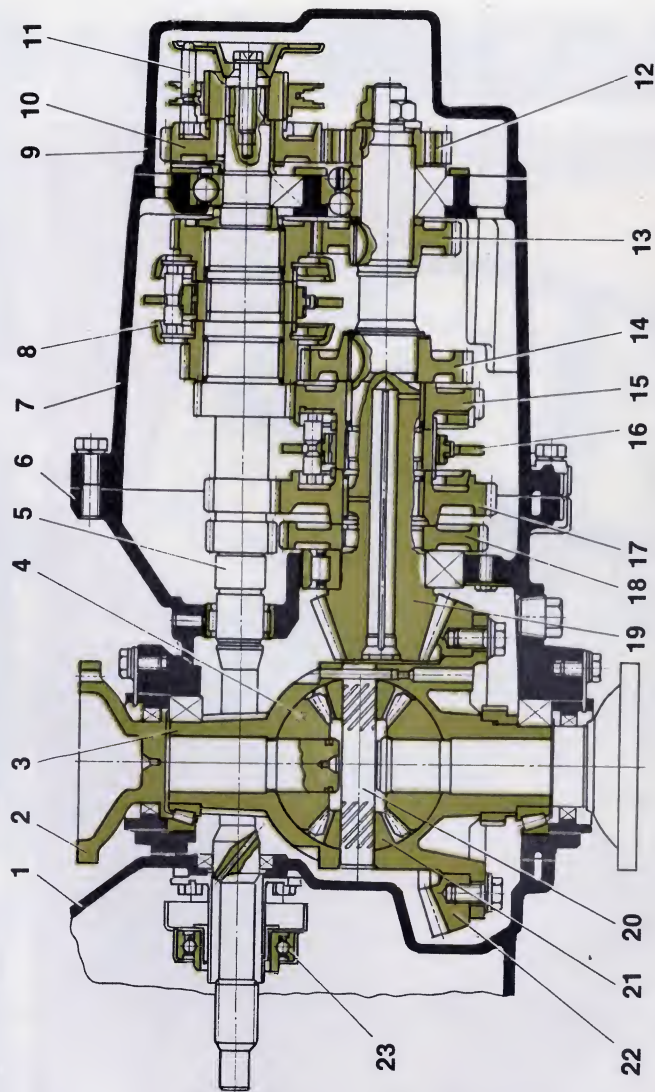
Трансмиссия «Москвича-2141»: 1 — картер сцепления; 2 — фланец полуоси; 3 — коробка дифференциала; 4 — шестерня полуоси; 5 — первичный вал; 6 — картер главной передачи; 7 — картер коробки передач; 8 — синхронизатор III и IV передач; 9 — крышка коробки передач; 10, 12 — шестерни V передач; 11 — синхронизатор V передач; 13 — ведомая шестерня IV передач; 14 — ведомая шестерня III передач; 15 — ведомая шестерня II передач; 16 — синхронизатор I и II передач; 17 — ведомая шестерня I передач; 18 — ведомая шестерня передачи заднего хода; 19 — вторичный вал с ведущей шестерней главной передачи; 20 — ось сателлитов; 21 — сателлит дифференциала; 22 — ведомая шестерня главной передачи; 23 — выжимной подшипник сцепления.
